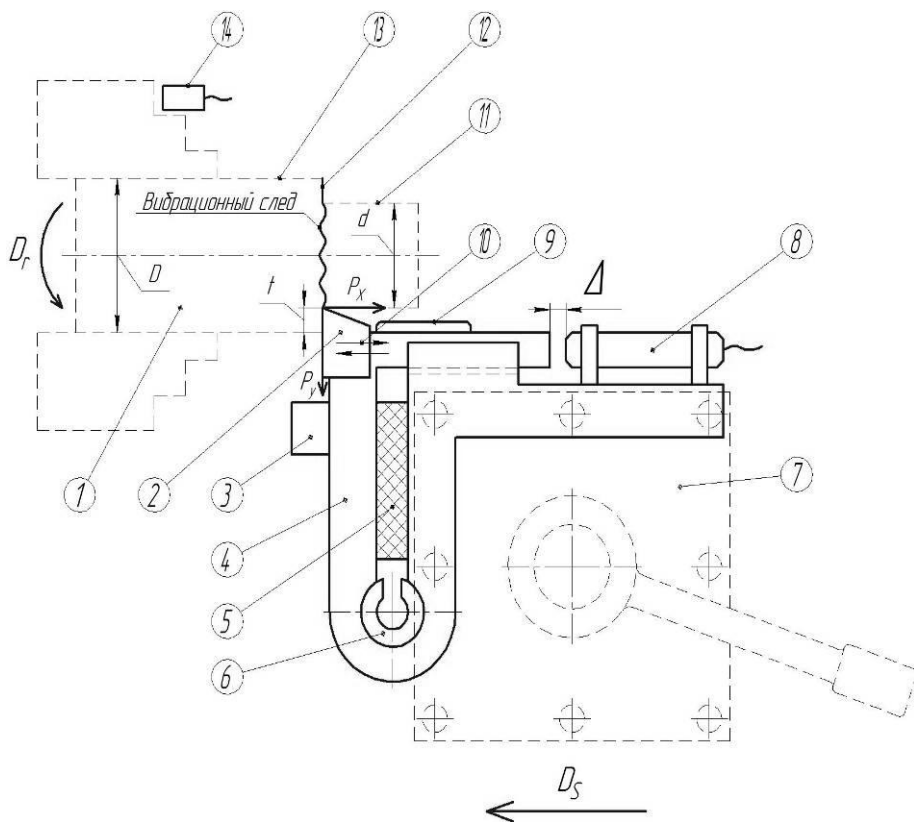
Принципиальная схема установки для изучения регенеративных колебаний при точении: 1 – деталь; 2 – режущая пластина; 3 – дополнительная масса; 4 – упругая державка режущей пластины; 5 – вязкоупругая среда (демпфер); 6 – сменная разрезная втулка для изменения жесткости; 7 – резцедержатель станка; 8 – бесконтактный токовихревой датчик перемещений; 9 – акселерометр; 10 – колебательные движения резца по оси X; 11 – обработанная поверхность; 12 – поверхность резания; 13 – обрабатываемая поверхность; 14 – отметчик оборотов детали
